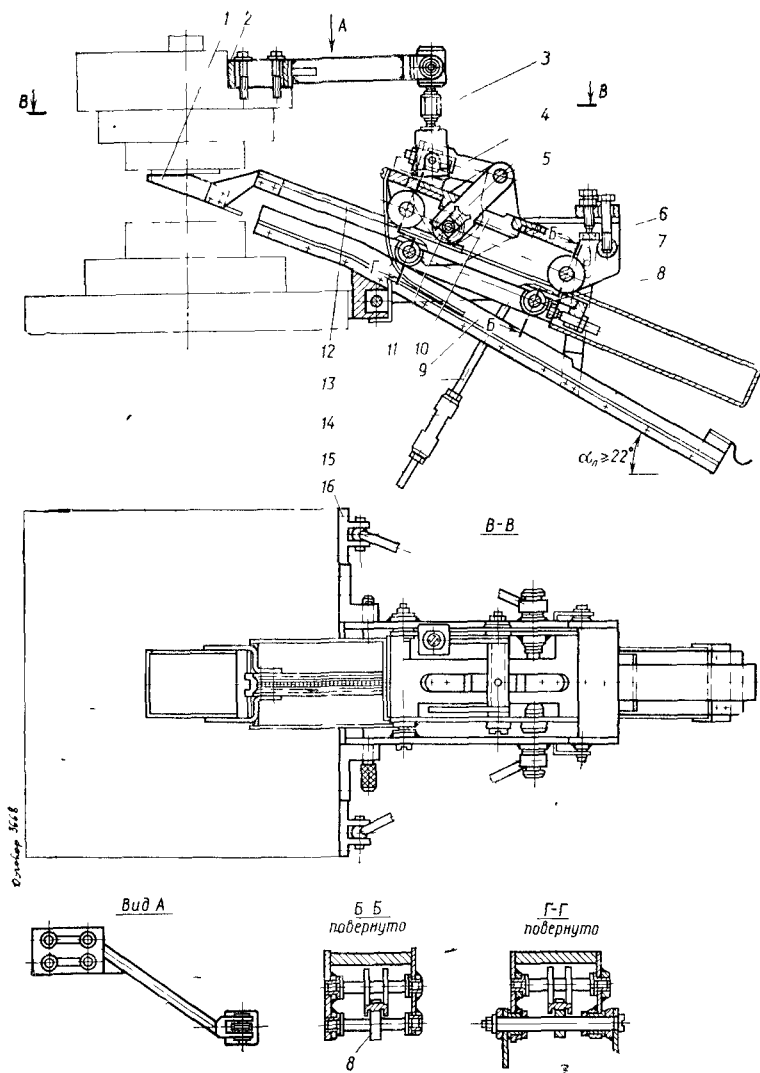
Выносящее устройство с шестеренно-реечным и рычажным механизмами
